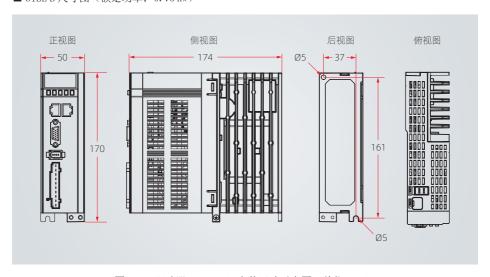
驱动器 (SIZE B) 安装尺寸示意图 (单位: mm)
